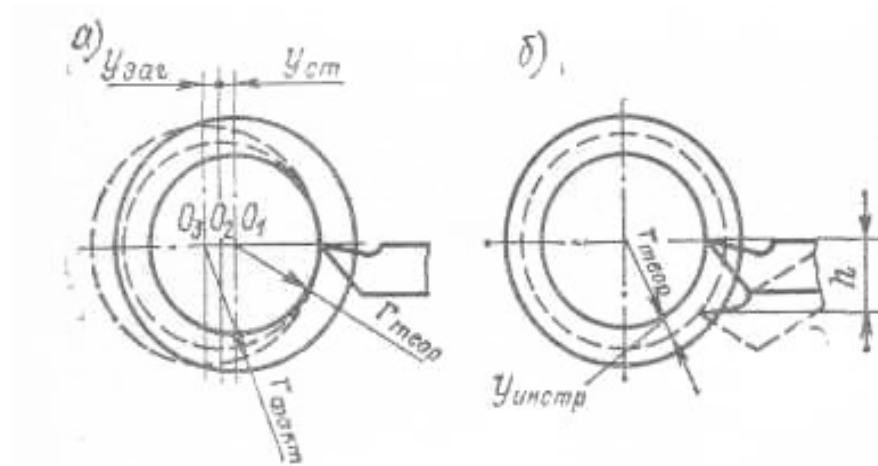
Вплив пружних деформацій на розмір оброблюваної заготовки:
